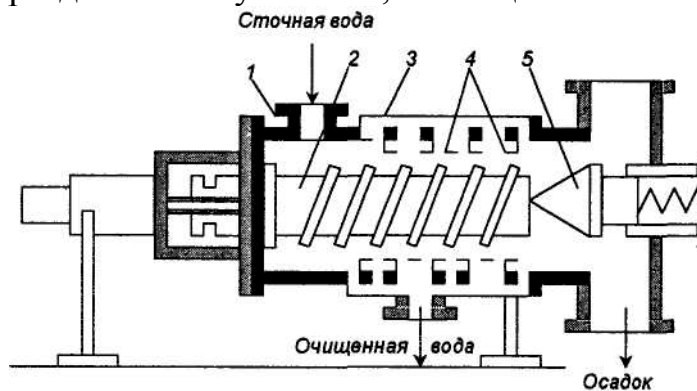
Червячный отжимной аппарат 1 — воронка; 2 — отжимной червяк; 3 — корпус; 4 — набор пластин; 5 — прижимная головка
